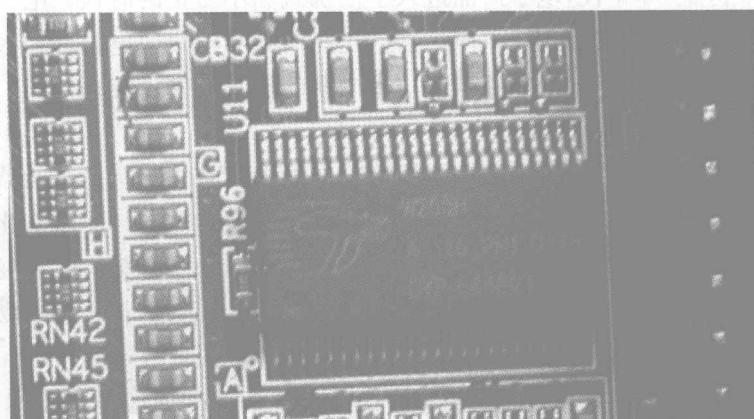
表面安装器件的 PCBA 的外形(SMA 的外形)
